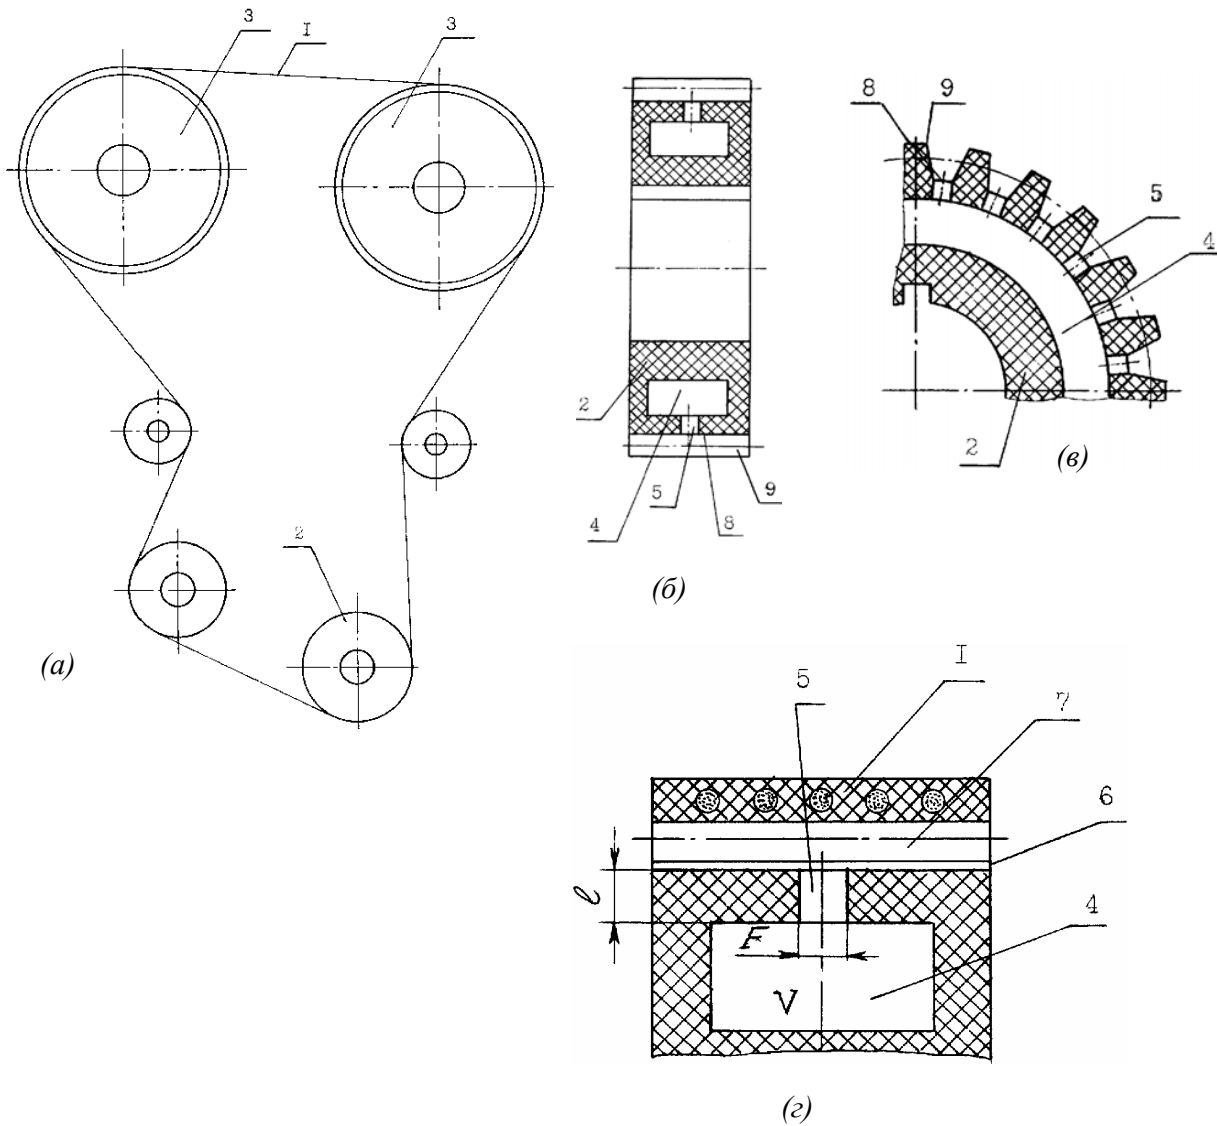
Схемы зубчато-ременного привода механизмов ДВС (а), сечения зубчатого колеса (шкива), в котором образован резонатор Гельмгольца (б, в), фрагмента привода в варианте охвата зуба колеса зубом ремня (г):
